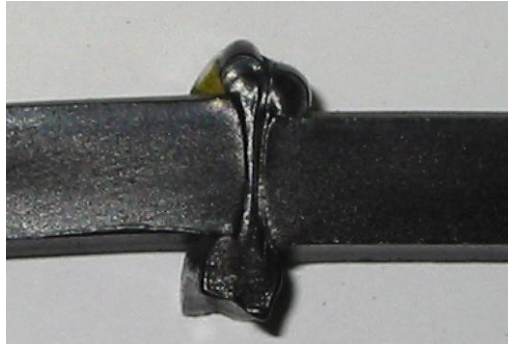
Aspectul macroscopic al unei probe extrase dintr-o îmbinare de țevi din PE 80, sudată cap la cap cu element încălzitor, ce prezintă un defect de tip bavură ascuțită [79]
